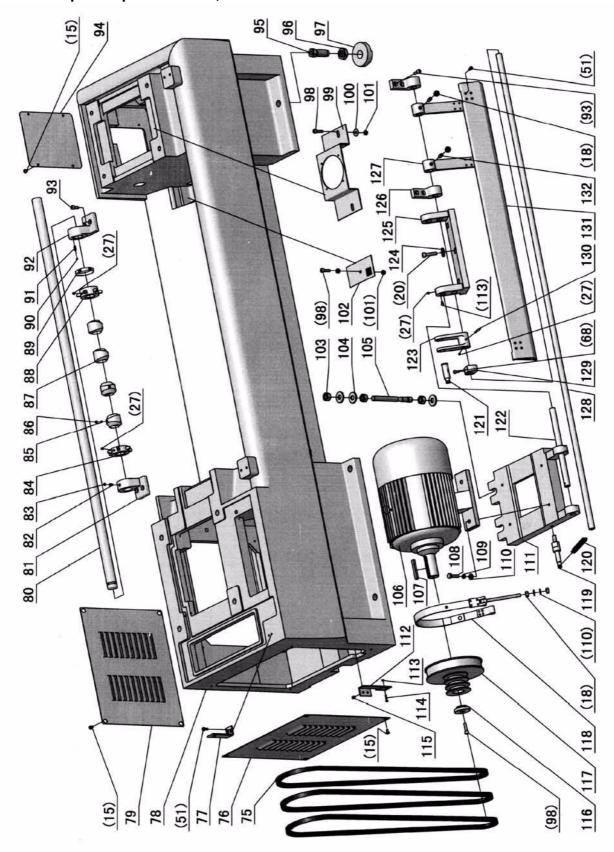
Mechanische Spindelbremse - Mechanical spindle break, actuation
